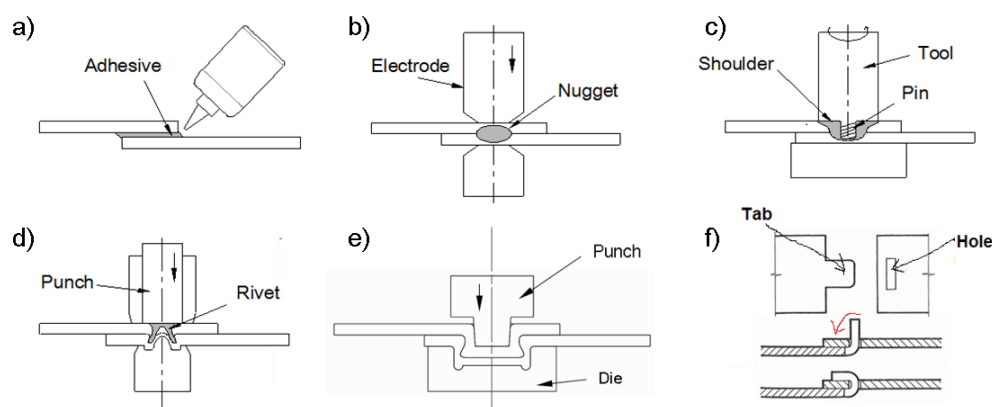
Processos atualmente utilizados na obtenção de juntas entre chapas sobrepostas: a) Tecnologia de adesivos; b) Soldadura por pontos (RSW); c) Soldadura por fricção linear por pontos (FSSW); d) Self-pierce Riveting (SPR); e) Clinching; f) Hemming.
